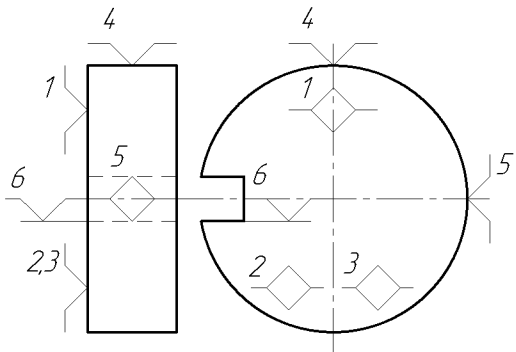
Теоретична схема базування коротких циліндричних деталей ($l < d$): 1,2,3 – установча база; 4,5 – подвійна опорна база; 6 – опорна база
